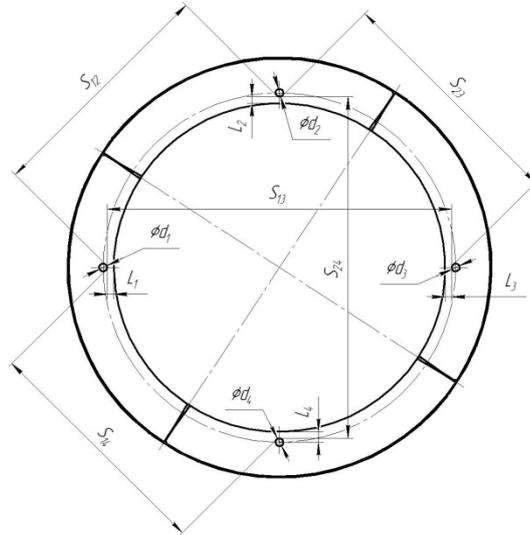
Схема измерений при контроле позиционного допуска на отверстия под штифты фланца стабилизирующей секции
